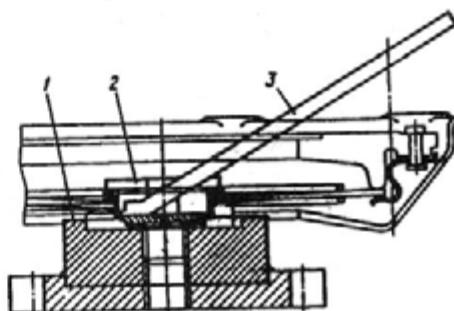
Общий вид комплекта ремонтного инструмента для установки опорной пяты:
